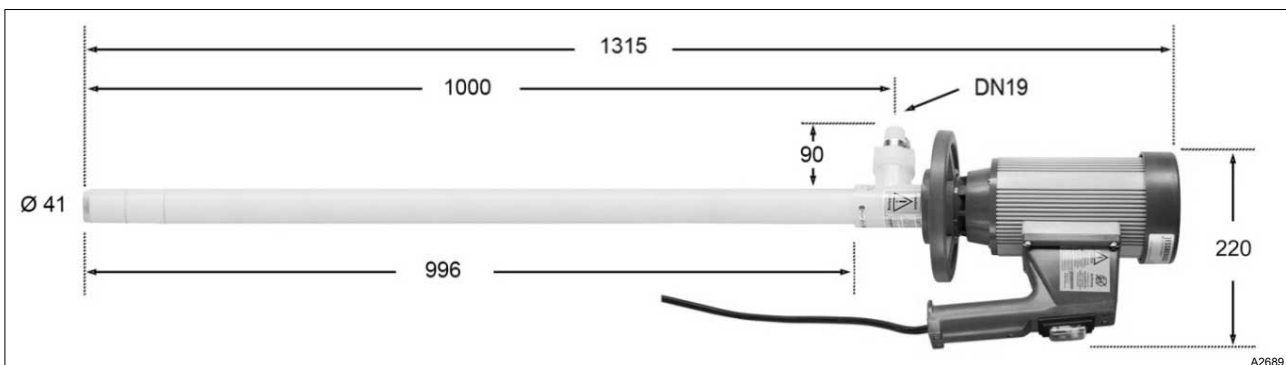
Ausführung PVDF: Maßzeichnung mit Hauptabmessungen, alle Angaben in mm.
